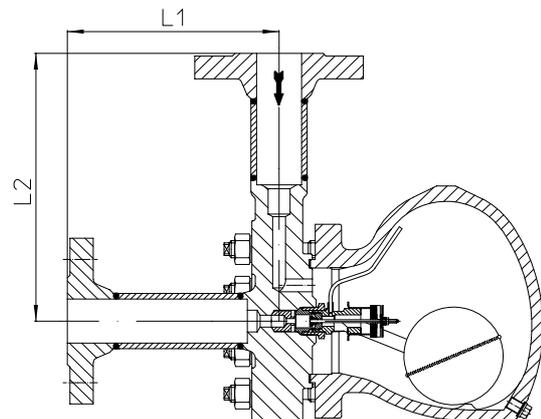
1 Eck-Ausführung mit Flanschen - vertikale Einbaulage
